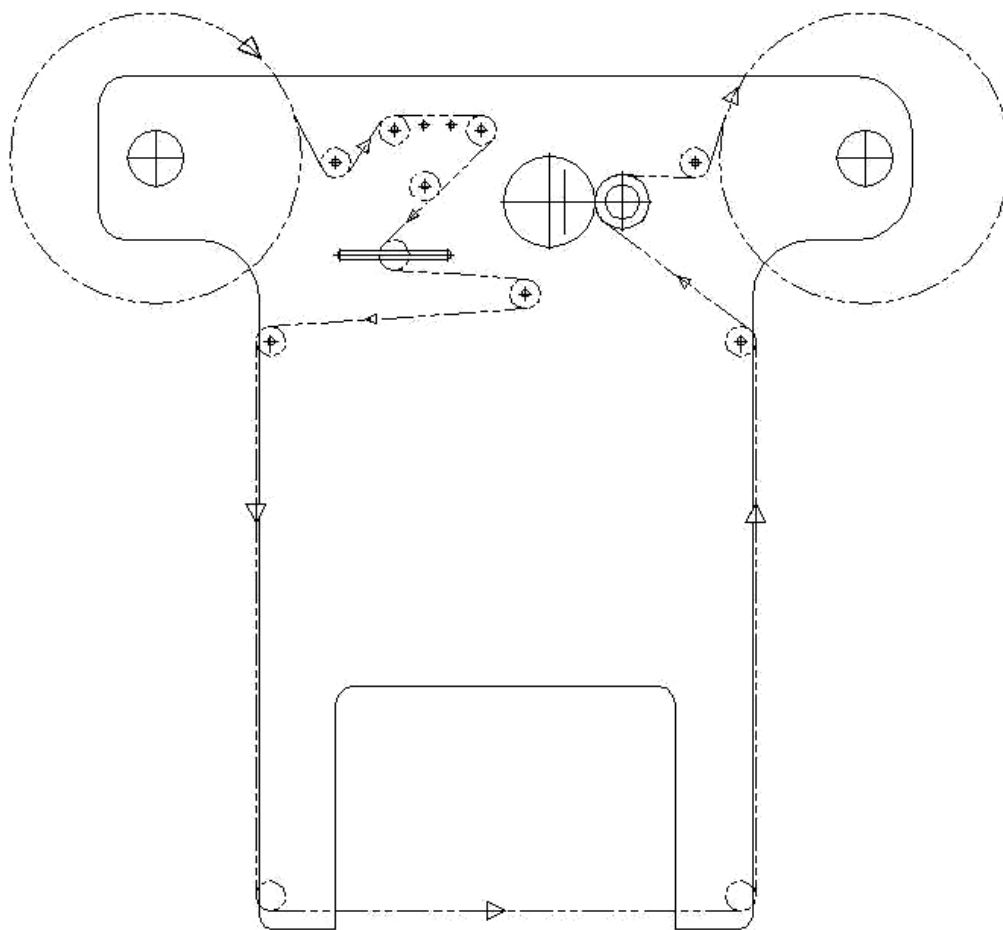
Схема протяжки и установки пленки для запаивания контейнеров
